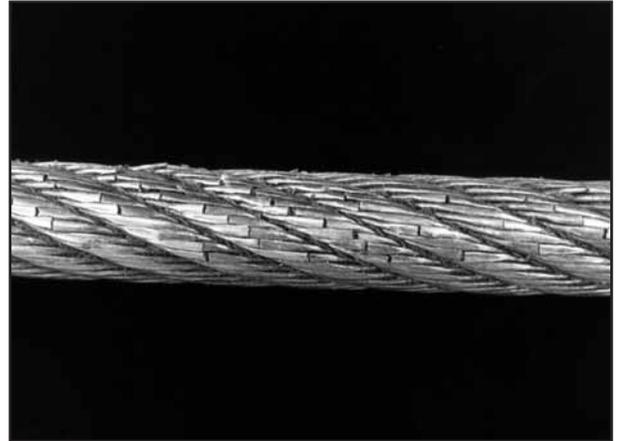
Ein weiteres Beispiel eines Seiles, welches in einer zu engen Seilscheibe gearbeitet hat.
